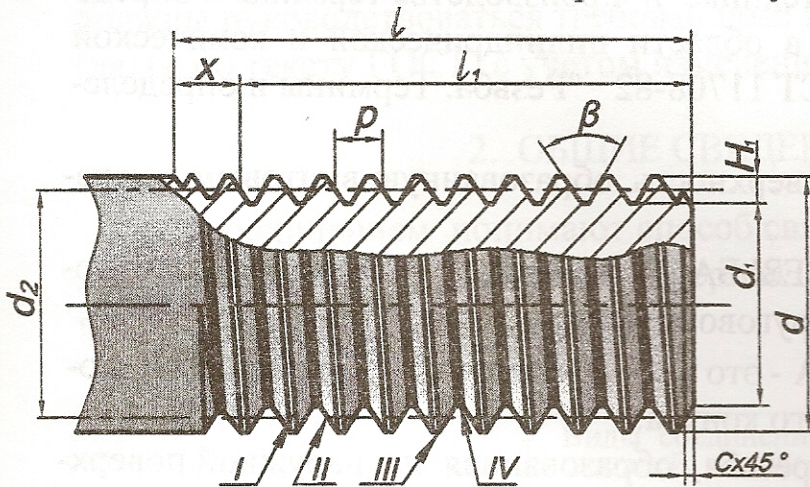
Наружная цилиндрическая резьба и ее параметры:
